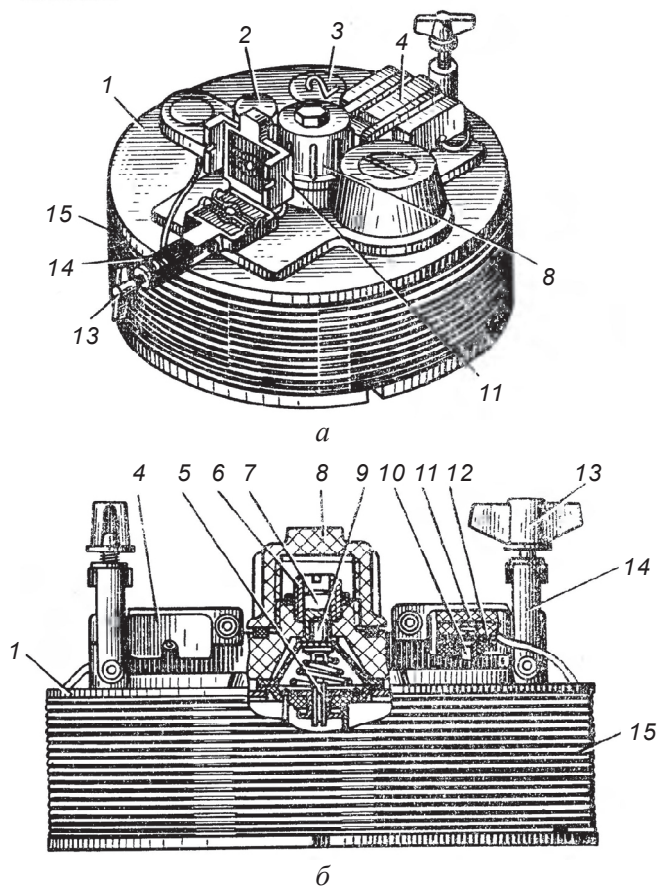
Исполнительный прибор [4, кн. 3, с. 161]:
